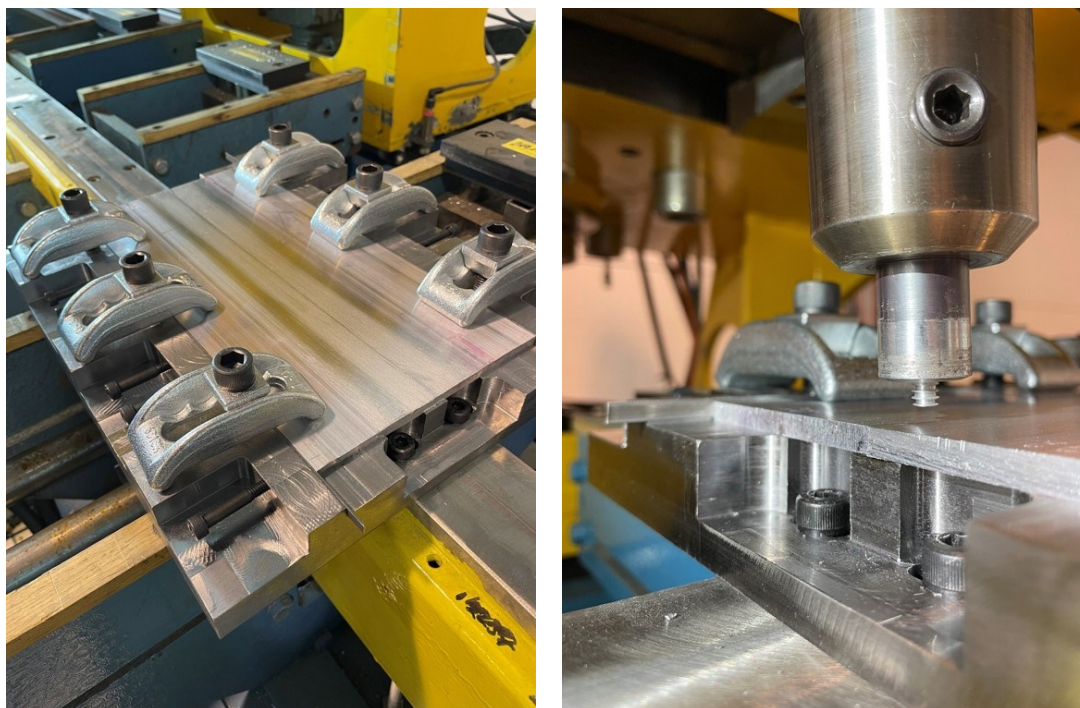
Sistema di bloccaggio e geometria dell'utensile (Sintef Manufacturing)
